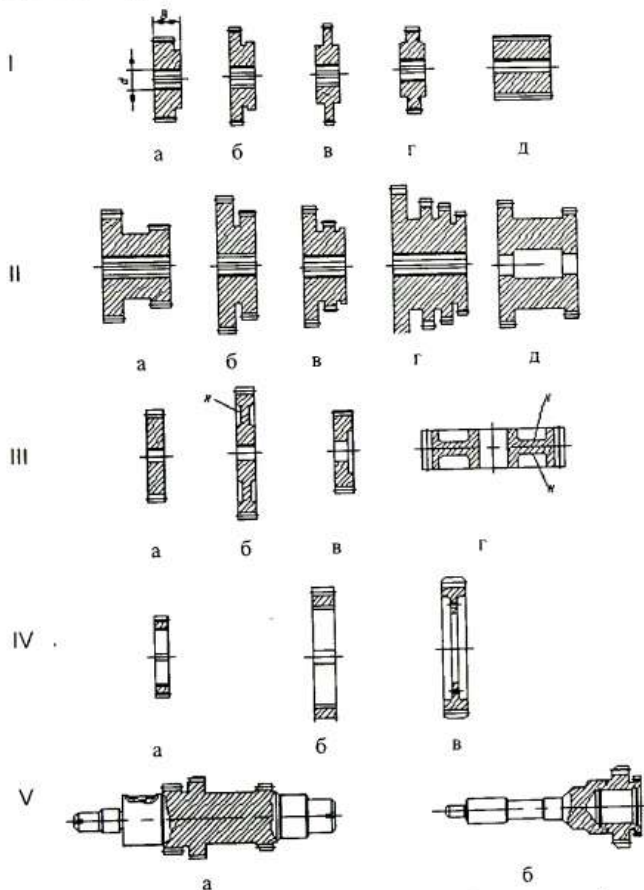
Різні типи циліндричних зубчастих коліс:
